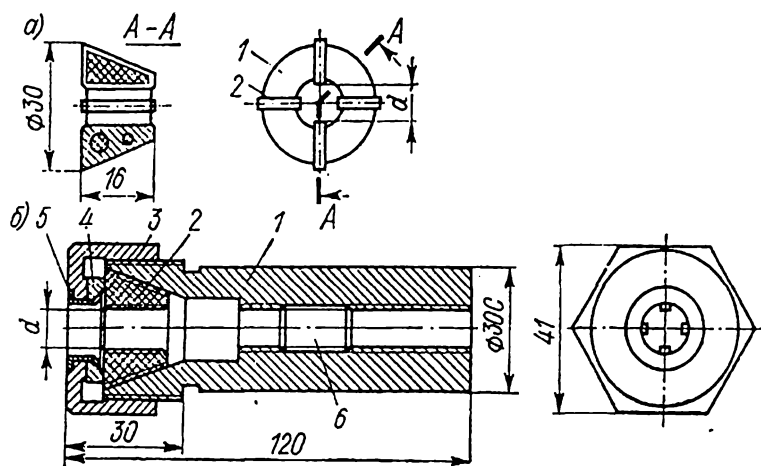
Цанговий патрон з гумово-металевою еластичною цангою:
